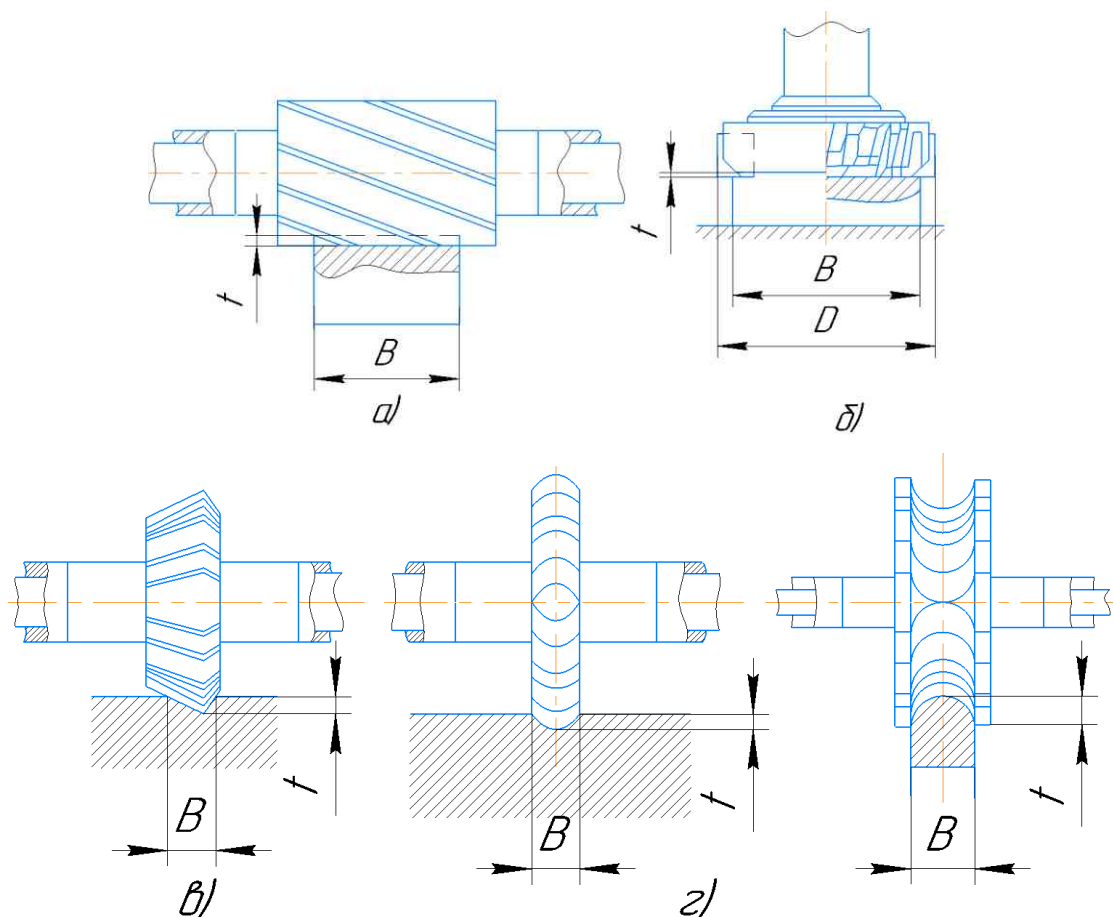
Види фрез по розташуванню зубців :: [5,с.81]
